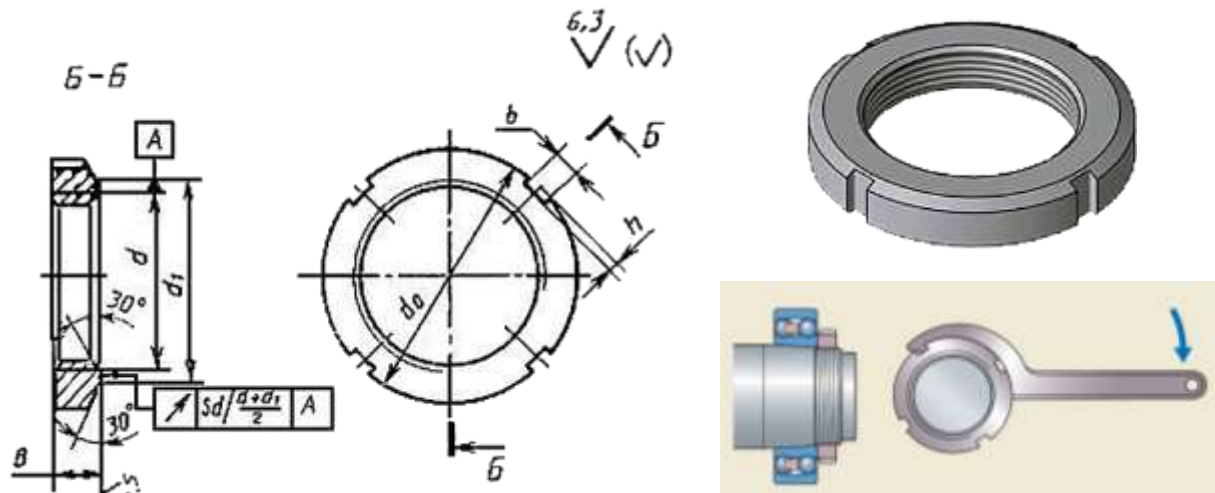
Пазова гайка (гайка кругла шліцьова згідно DIN 1804)
